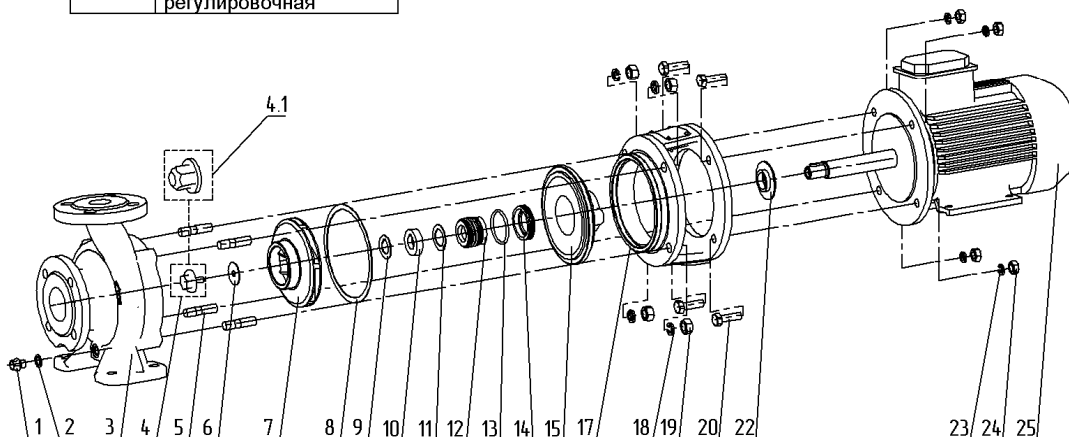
а – Устройство и схема разборки с торцовым уплотнением.
